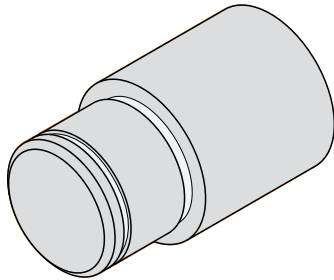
Exempelarbetsstycke – Finbearbeta ytterkontur
